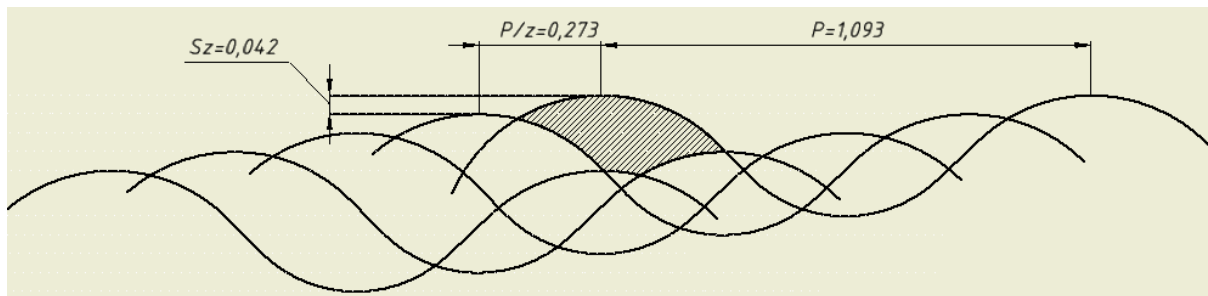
Образование сечения срезаемого слоя фрезой с криволинейной режущей кромкой *Preci Tool 166205*.
